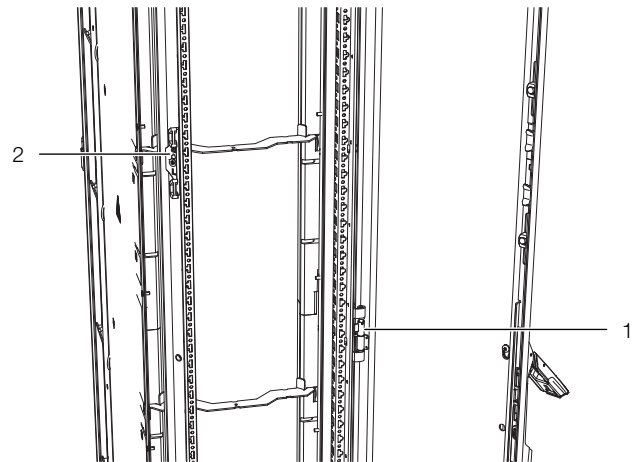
Befestigungselemente am Liquid Cooling Package – Rückansicht
